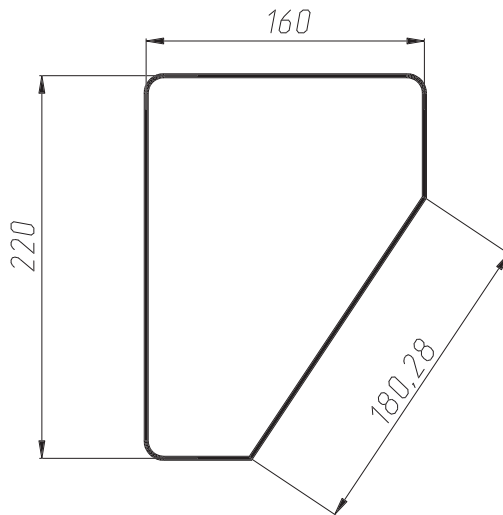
Горизонтальный, вертикальный и параллельный размеры
